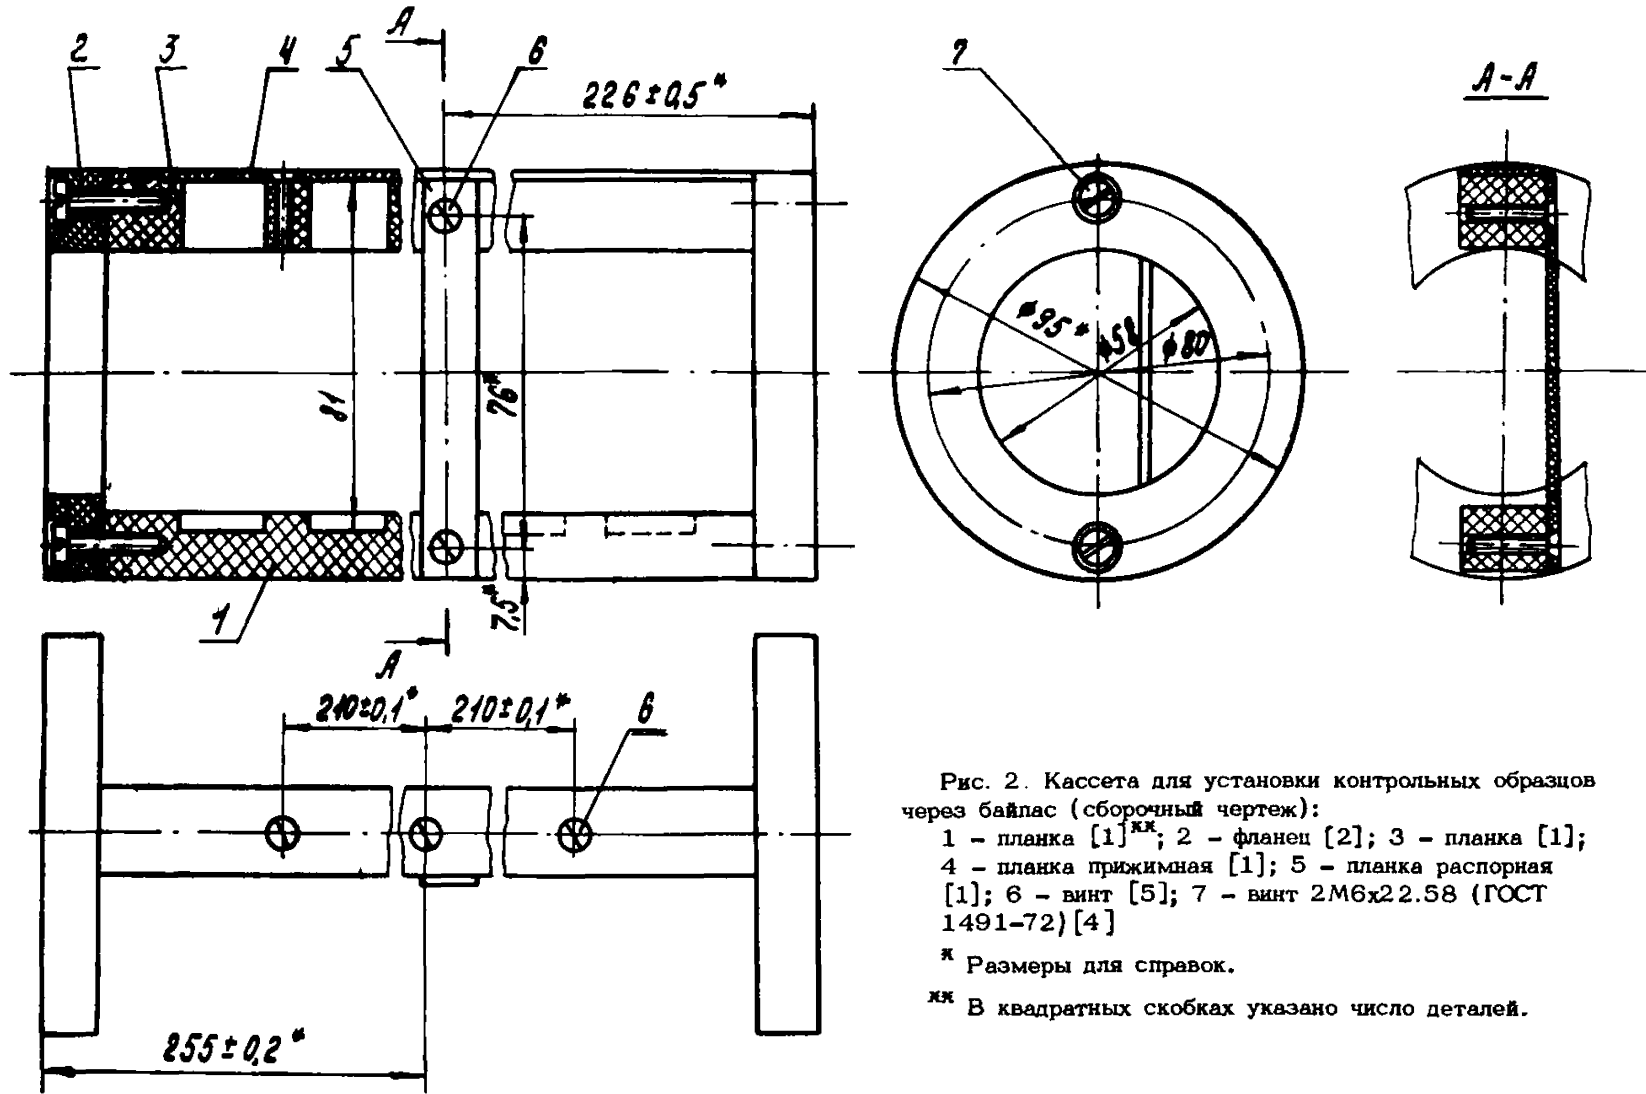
Кассета для установки контрольных образцов через байпас (сборочный чертеж):
